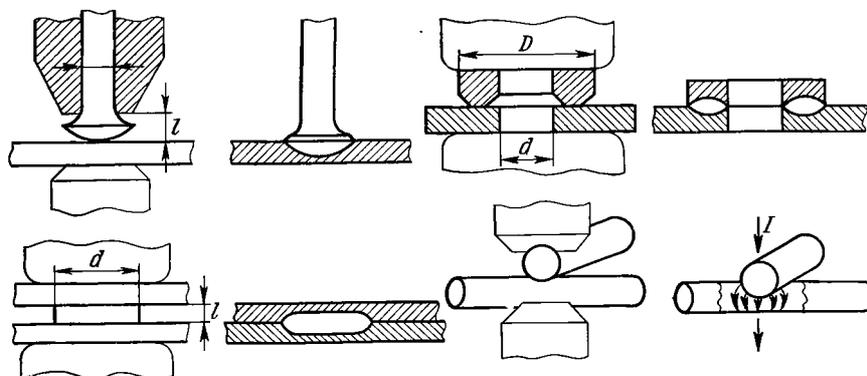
Некоторые типы рельефно-сварных соединений
